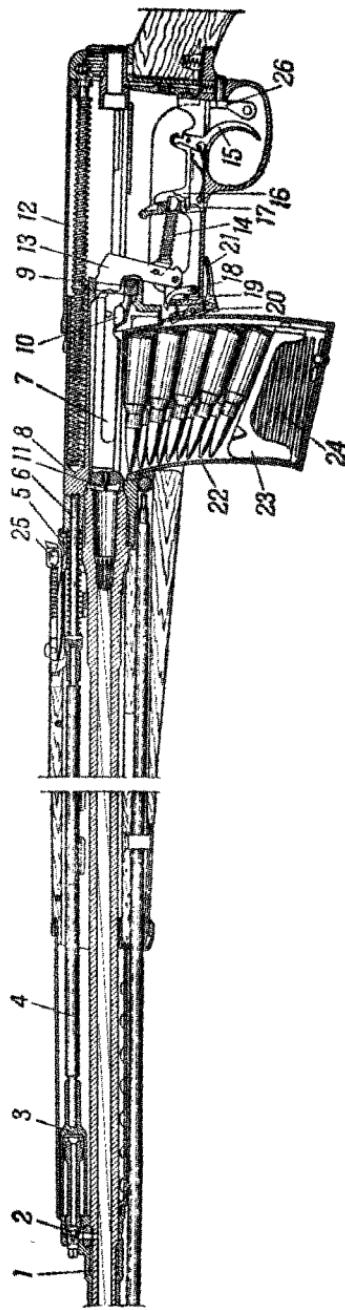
б. Положение механизмов СВТ-40 до заряжания: 1 - ствол; 2 - газовая камера с регулятором и патрубком; 3 - газовый поршень; 4 - шток; 5 - пружина толкателя; 6 - толкатель стебля затвора; 7 - затвор; 8 - стебель затвора; 9 - отпорный вкладыш ствольной коробки; 10 - пружина толкателя стебля затвора; 11 - болт ударника; 12 - взрыватная пружина; 13 - курок; 14 - боевая пружина; 15 - спусковой крючок; 16 - выступ спусковой тяги; 17 - коромысло; 18 - автоматический спуск; 19 - пружина автомата спуска; 20 - защелка магазина; 21 - хвост защелки; 22 - магазин; 23 - подаватель; 24 - пружина подавателя; 25 - хомутник пружиной планки; 26 - предохранитель.
